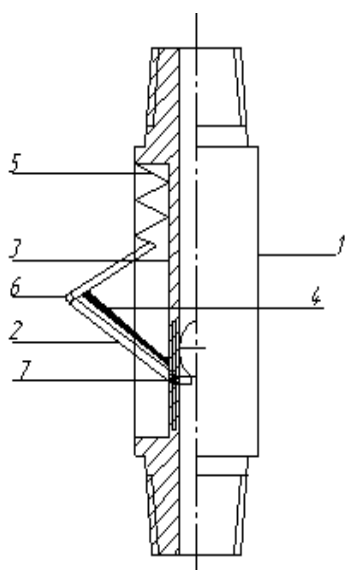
Схема пристрій для оброблення стовбура свердловини
